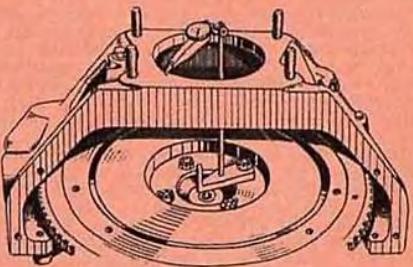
А так — перпендикулярность заднего торца картера сцепления к оси коленчатого вала.
